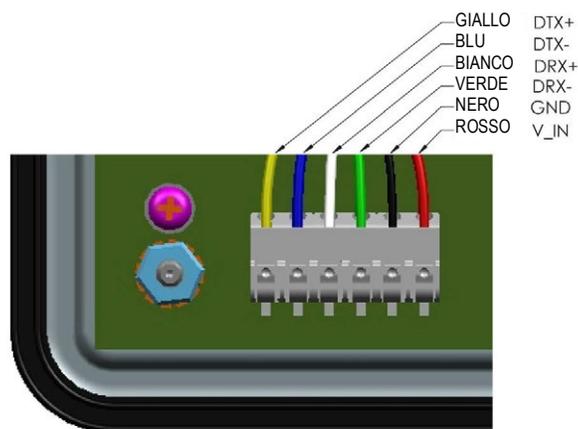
Dettaglio del collegamento del fascio di cavi
